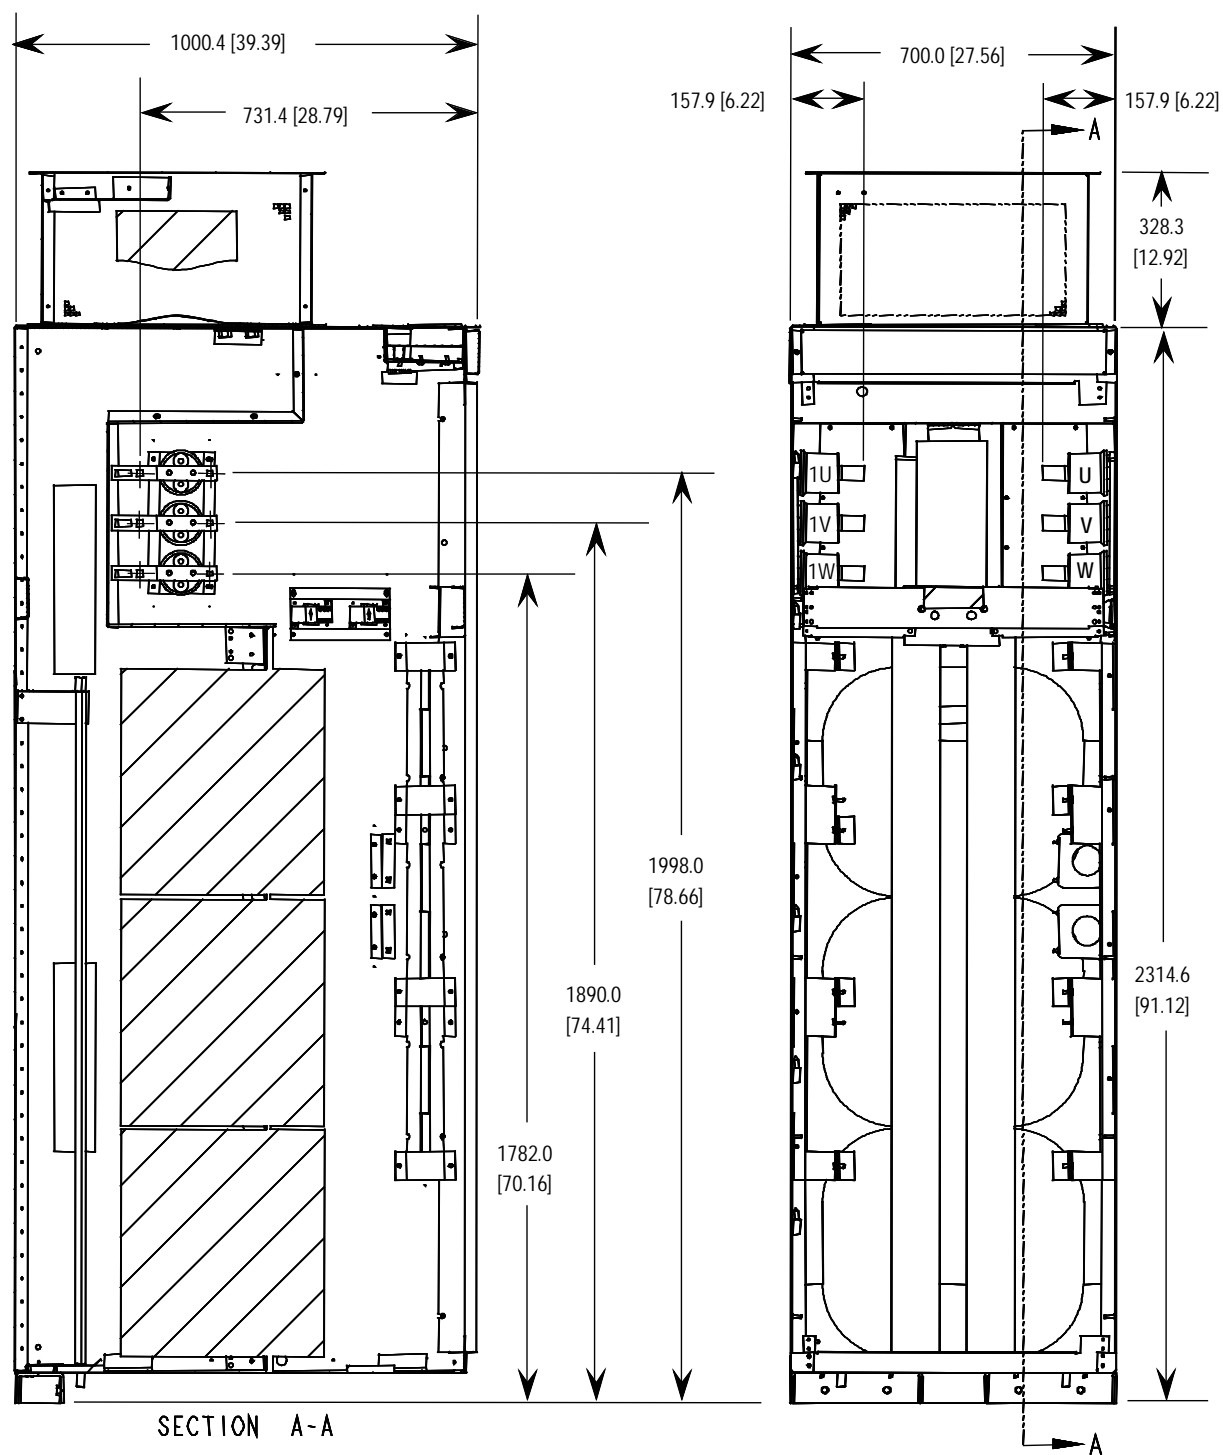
Viste dimensionali dell'armadio di cablaggio per la Configurazione 3
